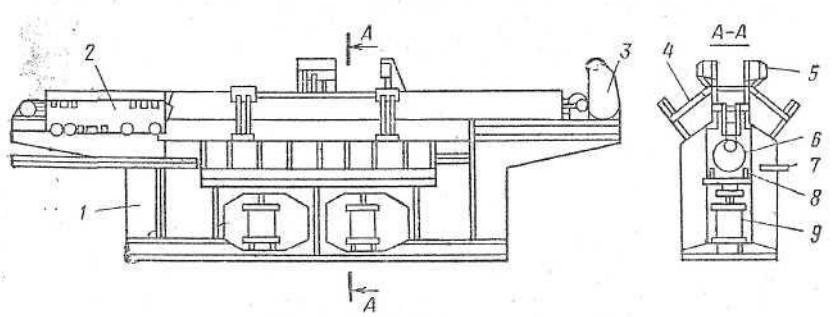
Полуавтомат СТД- 363 для изготовления круглых фальцевых воздуховодов
